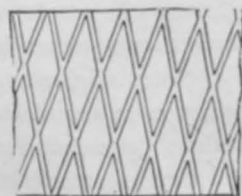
Riffelblech mit eingewalzten rautenförm. Vertiefungen.
